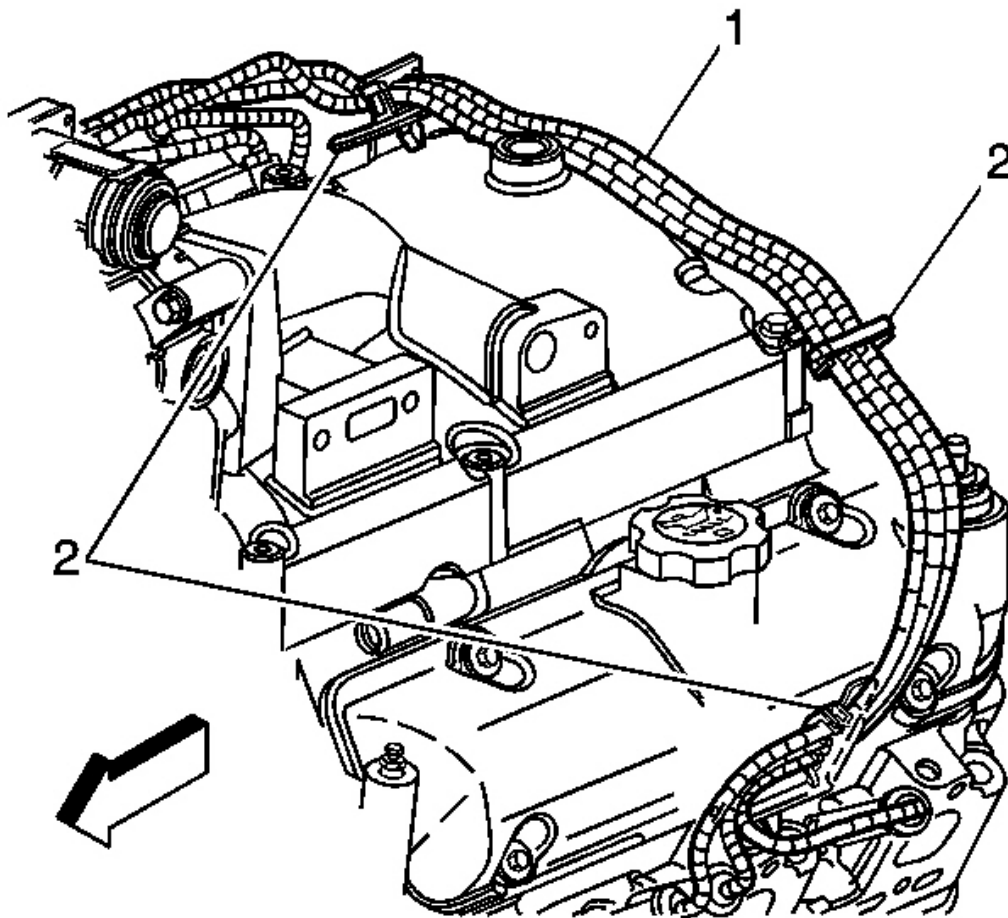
Vista de cable de la bujía Soporte y Perno
